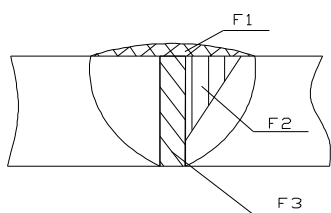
Схема расчета поперечной плоскости сварочного шва.
